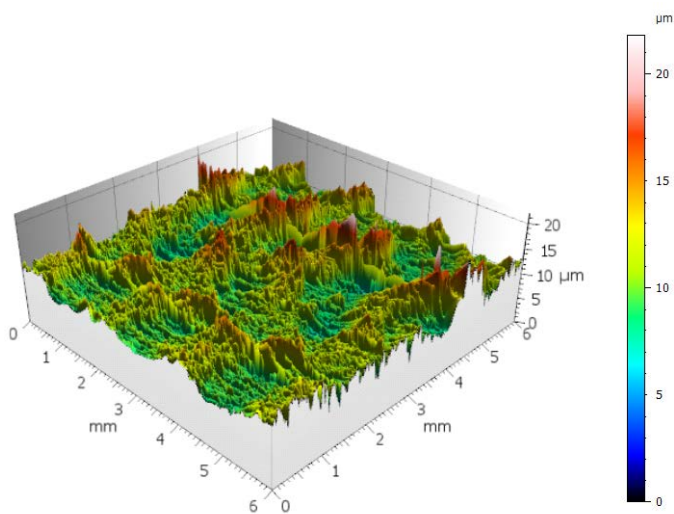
Топографія обробленої поверхні після фрикційної обробки інструментом з різнонаправленими пазми на робочій поверхні
